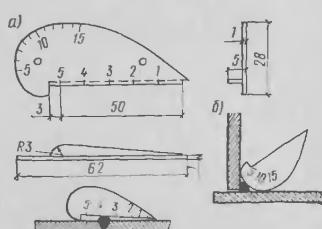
Универсальный шаблон А. И. Красовского для проверки формы и размеров сварных швов
